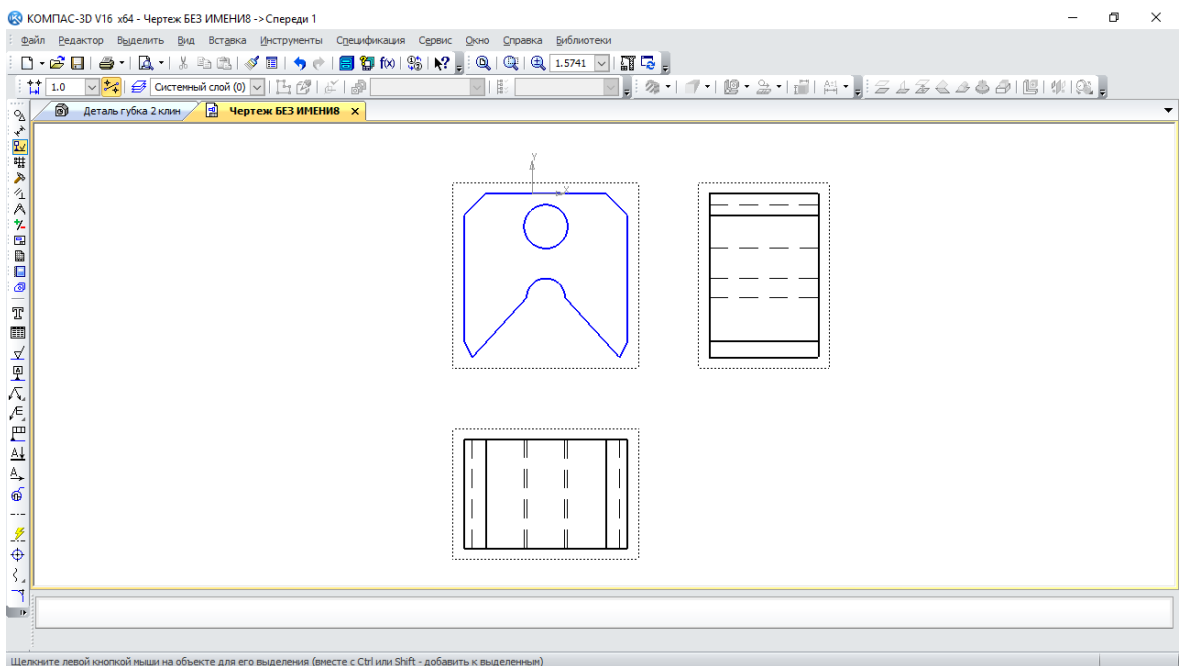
Модель 2D губок пристрою захоплення типу клин
